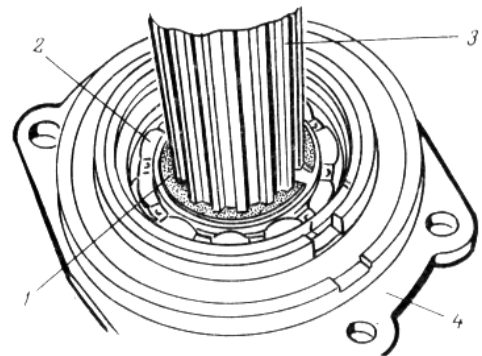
Знімання стопорного кільця підшипника первинного вала: 1- стопорне кільце; 2- підшипник; 3- первинний вал; 4- стакан первинного вала
